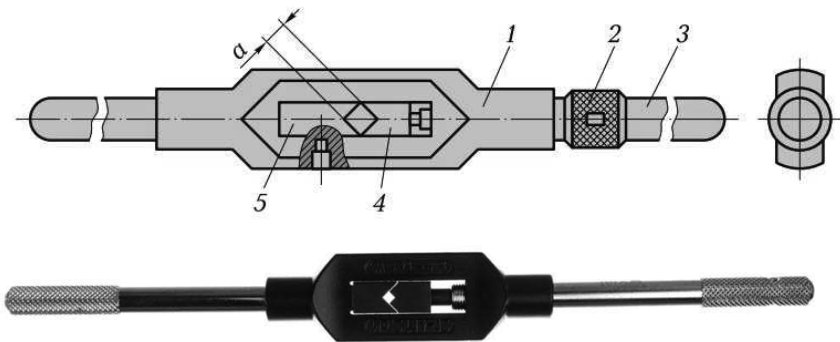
Розсувний вороток: 1 – рамка; 2 – муфта; 3 – рукоятка; 4, 5 – відповідно рухливий і нерухомий сухар; а – сторона квадрата
